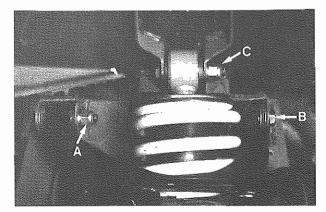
A - Viti fissaggio braccio sup. al telaio Screws fixing upper arm to frame
